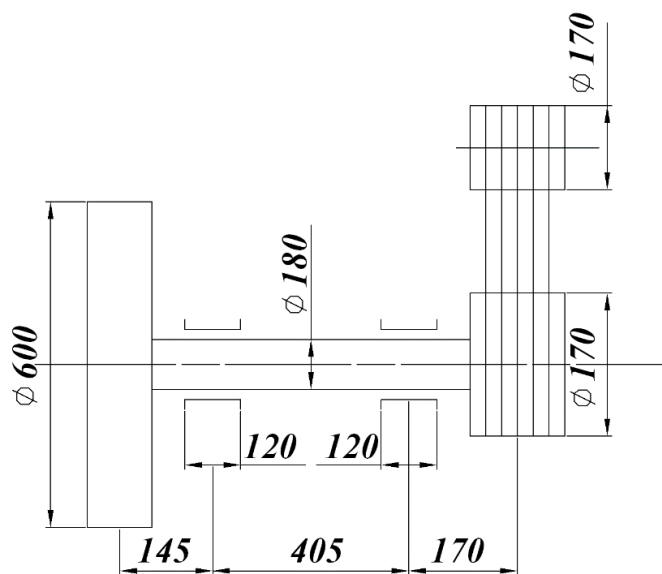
Схема приводу круга і розміри підшипників
